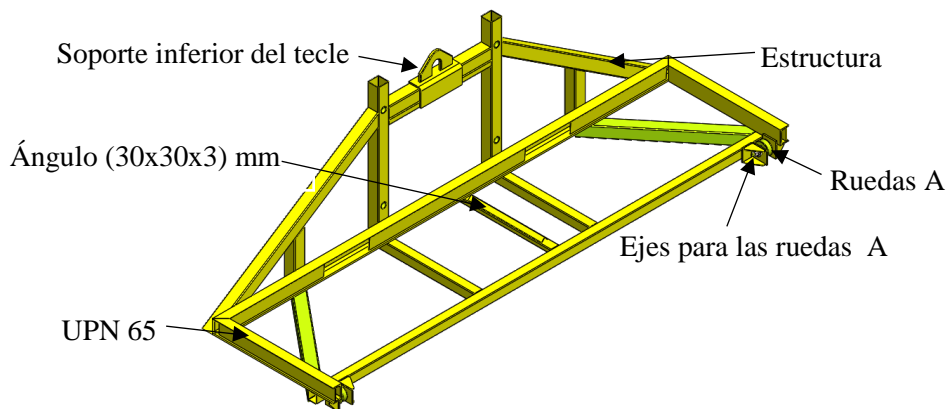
Elementos de la estructura soporte a la canasta de elevación
